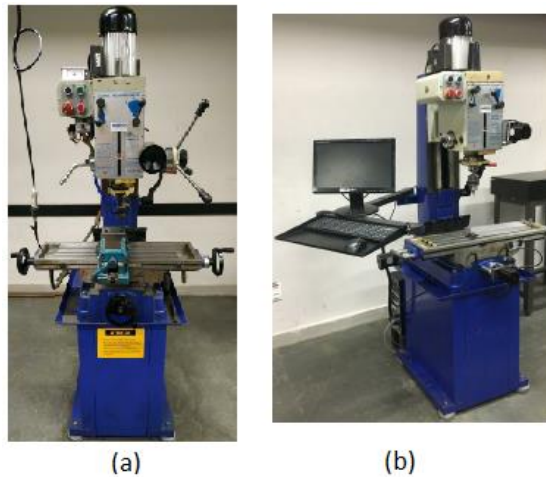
(a) Fresadora manual, (b) Fresadora CNC
